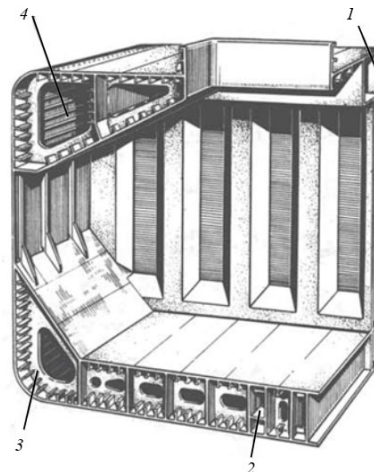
Комбінована поздовжньо-поперечна система набору корпусу балкерів: 1 - коробчаста поперечна балка; 2 – тунель затоплення; 3 - днищова бортова цистерна; 4 - підпалубна цистерна [11]
